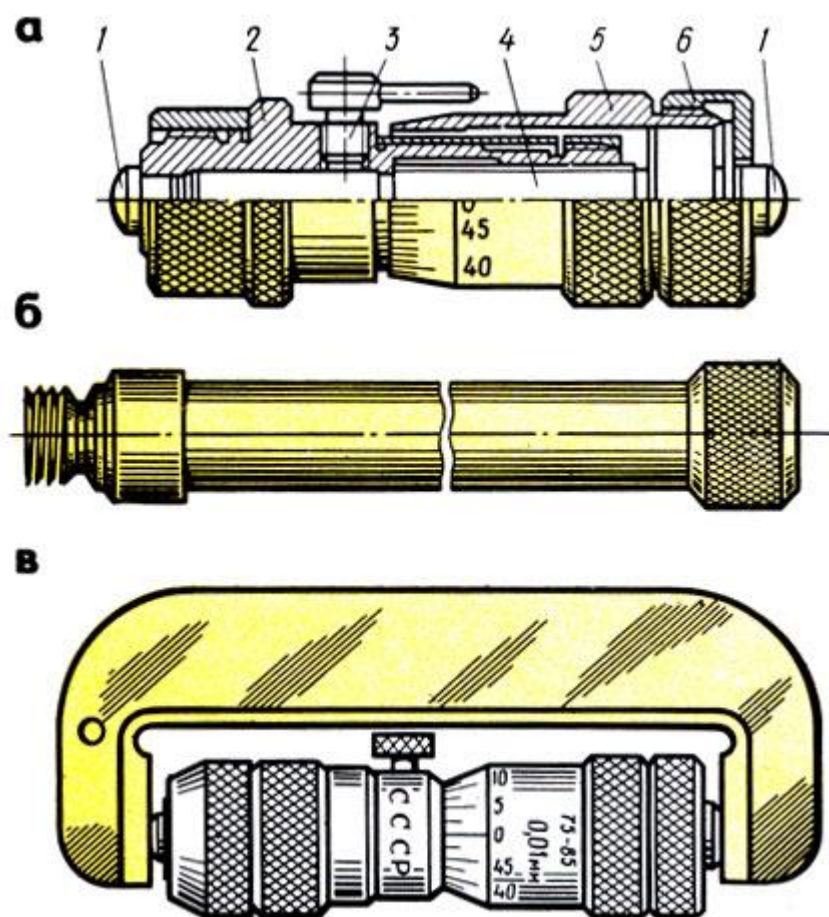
Микрометрический нутромер (штихмасс): а - устройство, б - удлинительный стержень, в - проверка нулевого положения; 1 - измерительные поверхности, 2 - стембель, 3 - стопор, 4 - микрометрический винт, 5 - барабан, 6 - гайка
